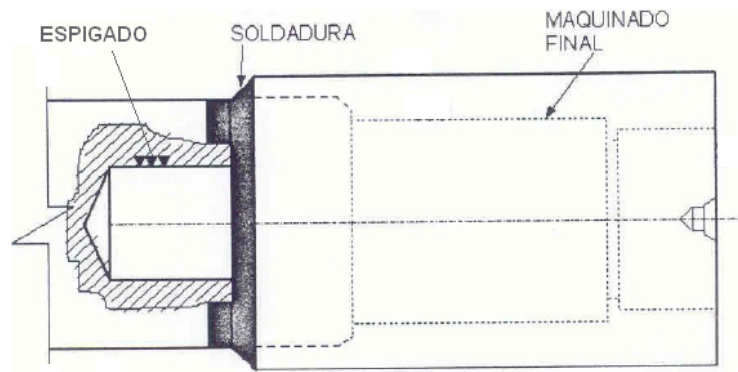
Esquema de la unión ensamblada por espigado y soldadura.
